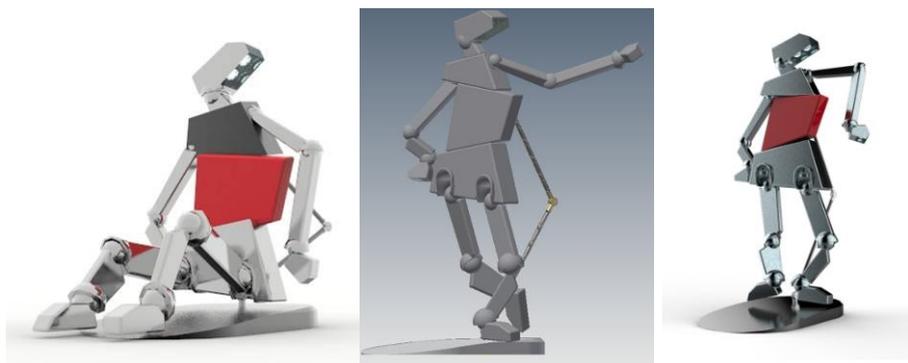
Первоначальный корпус лампы, плечо штатива и его установка
